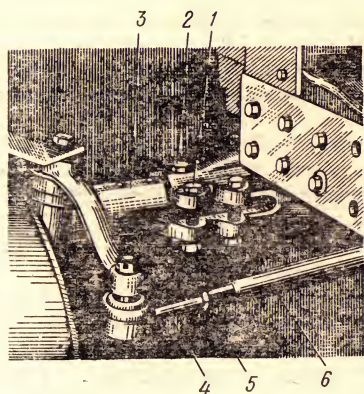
Изменение колеи передних колес трактора ЮМЗ-6: 1 — болт; 2 — стопор; 3 — выдвигающий кулак; 4 — наконечник; 5 — контргайка; 6 — труба
